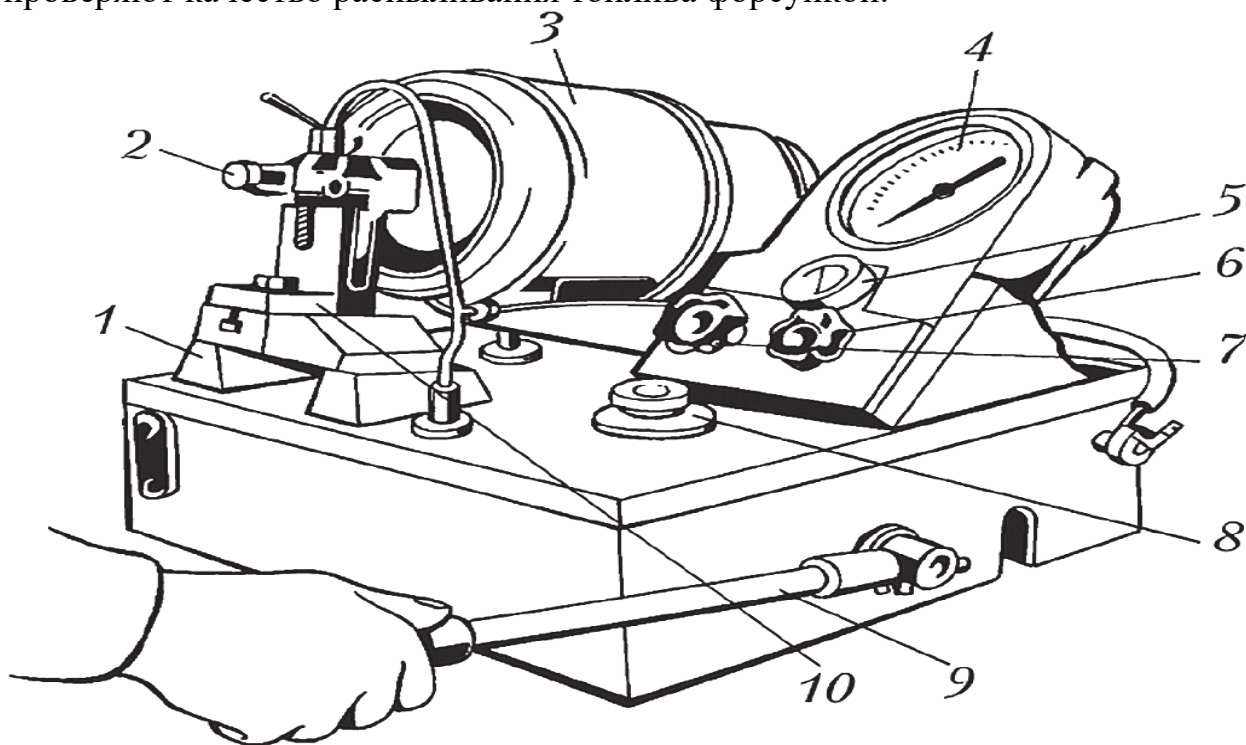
Общий вид стенда для испытания форсунок КИ-3333А: 1 — корпус; 2 — форсунка; 3 — камера впрыскивания; 4 — манометр; 5 — секундомер; 6, 7 — рукоятки клапанов соответственно манометра и насоса; 8 — пробка заливной горловины для топлива; 9 — рукоятка привода насоса; 10 — устройство для крепления форсунки
